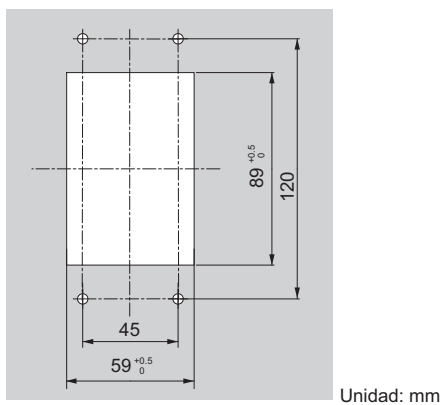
Dimensiones de corte del panel (instalación de montaje interno/embutido)
